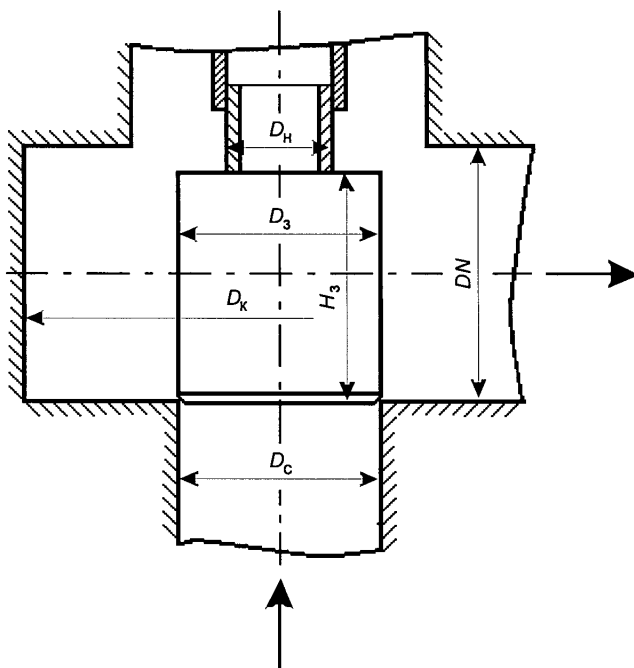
Обратный подъемный угловой клапан, ЗЭл с направлением в крышке
